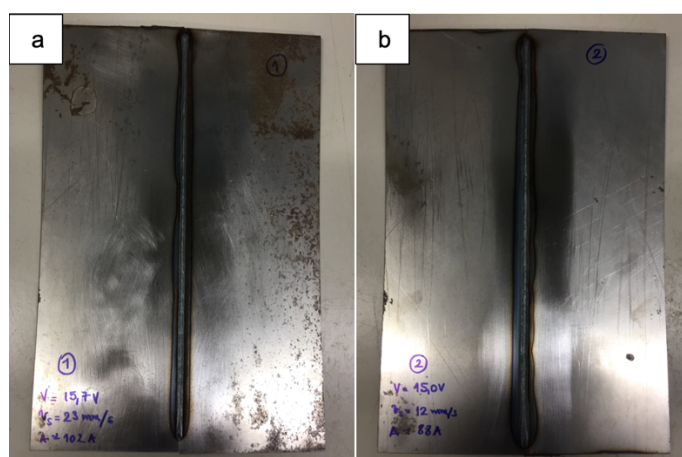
a) Chapa de HARDOX 450 soldada pela configuração MAG23. b) Chapa de HARDOX 450 soldada pela configuração MAG12.
